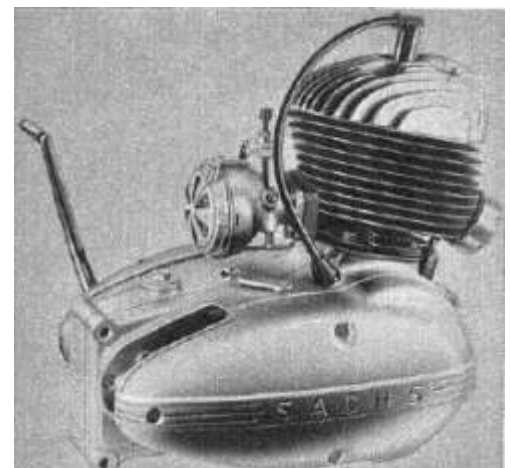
rechts: Der Gehäusedeckel rechts verdeckt nicht nur den Schwungradmagneten, dessen Lichtleistung von 30 Watt früher nur von reinen Gleichstrommaschinen erreicht wurde, sondern auch das Antriebsritzel der Hinterradkette. Da dieser Motor in Maschinen eingebaut werden wird, die fast ausnahmslos Teleskoptagel haben werden, hat man in diesem Deckel auch den Tachoantrieb untergebracht, der mit seinem Zweikant in einen Schlitz der Getriebehauptwelle hineingreift. Der Tachoantrieb von der Vorderradnabe her läßt sich nämlich bei Telegabeln schlecht ausführen, weil hier die Antriebswelle beim Durchfedern immer sehr stark gebogen wird. Der Antrieb vom Hinterrad verlangt aber eine doppelt so lange Antriebswelle wie hier, wo die Welle schräg nach vorne unten aus dem Deckel herausgeführt wird und sich dann dem vorderen Rahmenrohr anschmiegt.
